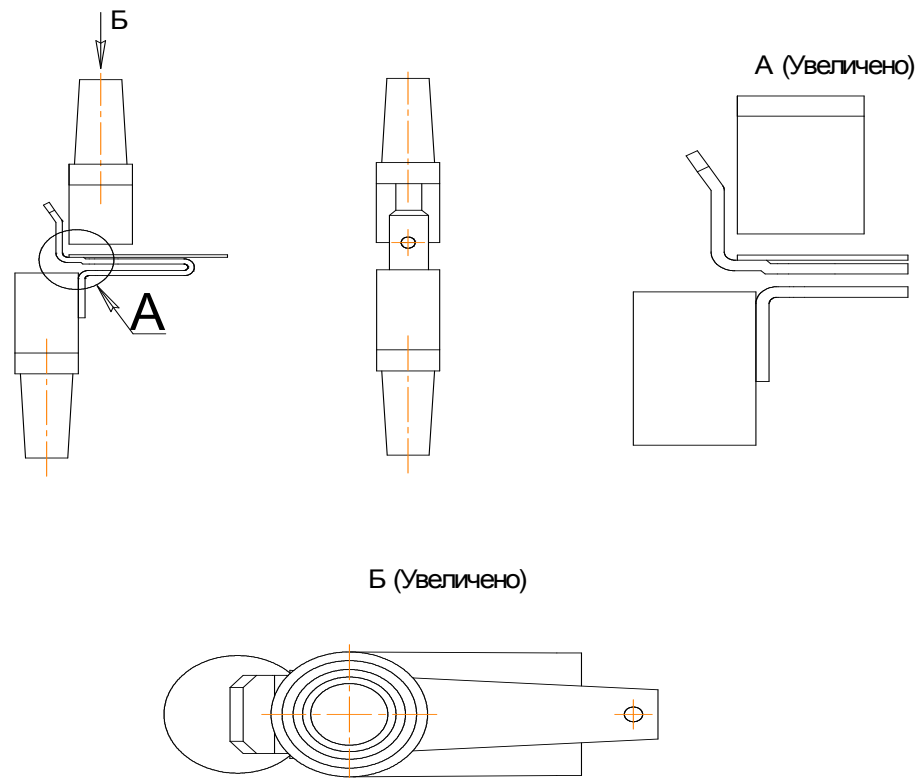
Сборка стальной скобы и пластины под сварку
